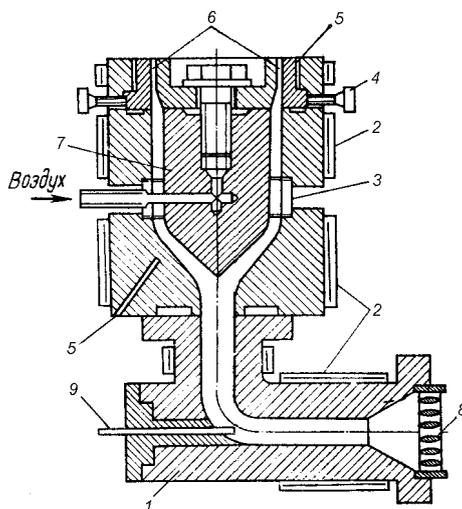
Схема угловой кольцевой головки для экструзии рукавной пленки: 1 – корпус; 2 – нагреватели; 3 – дорнодержатель; 4 – регулировочный болт; 5 – пазы для термопар; 6 – профилирующий канал; 7 – дорн; 8 – решетка и сетки; 9 – термопара для расплава.
